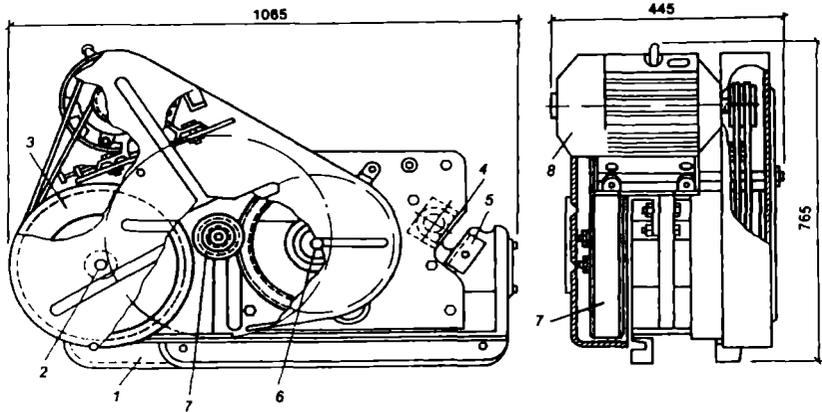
Станок СМЖ-172А для резки арматурной стали:
